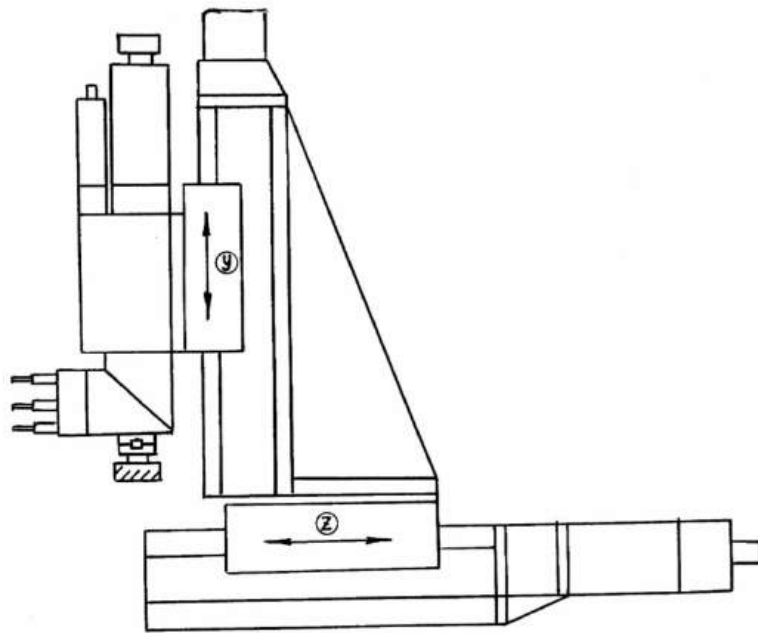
Двохкоординатний модуль з револьверною головкою
